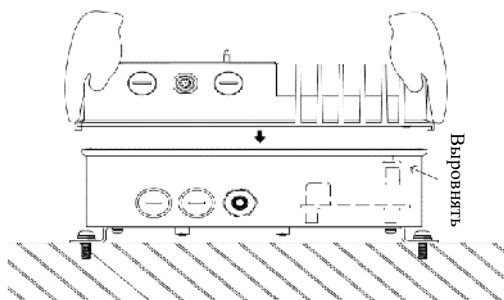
Установка средней части корпуса обратно на соединительную коробку
